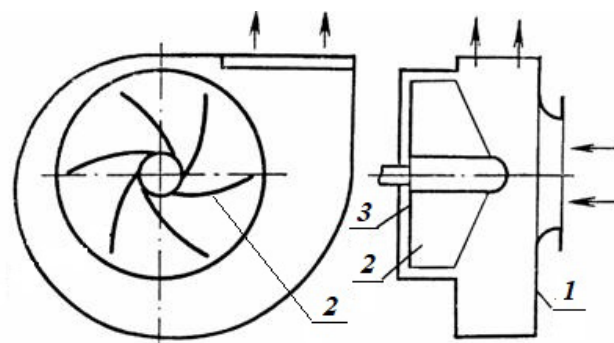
Схема смерчевой вентилятора: 1 — кожух; 2 — лопатка; 3 — задний диск
